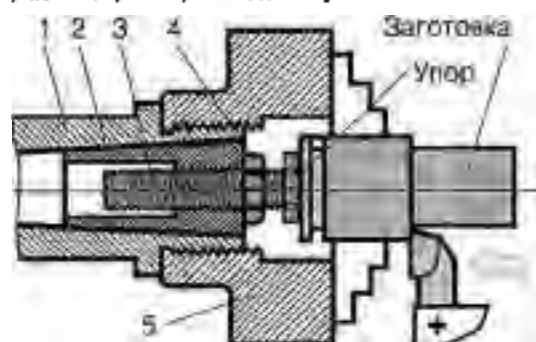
ШПИНДЕЛЬНИЙ УПОР
